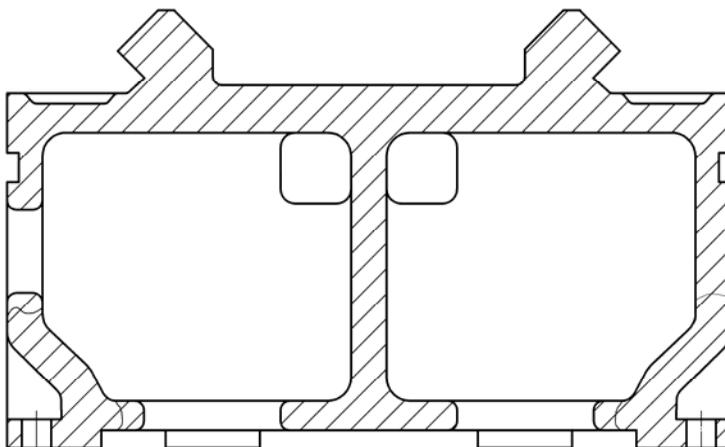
Замкнутый профиль поперечного сечения станины зубофрезерного полуавтомата
